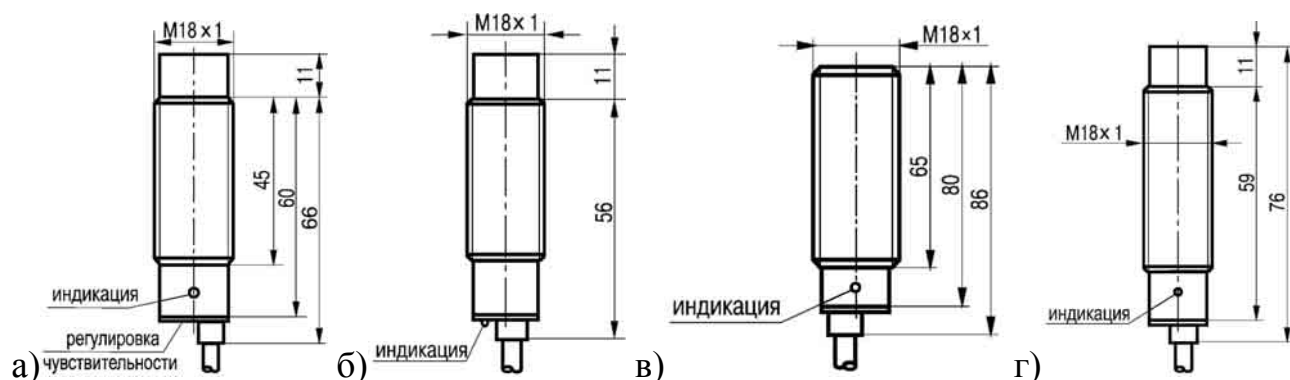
Внешний вид и габаритные размеры выключателей
